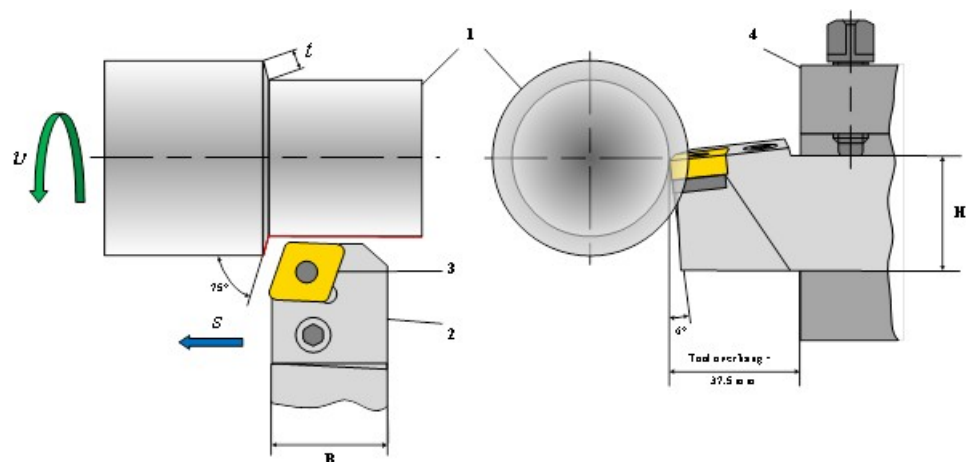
Схема обробки деталі: 1 – Деталь, яка обробляється; 2 – різальний інструмент (PCBNR-4040S-19), 3 – ріжуча вставка (CNMG 190616); 4 – тримач інструменту.
